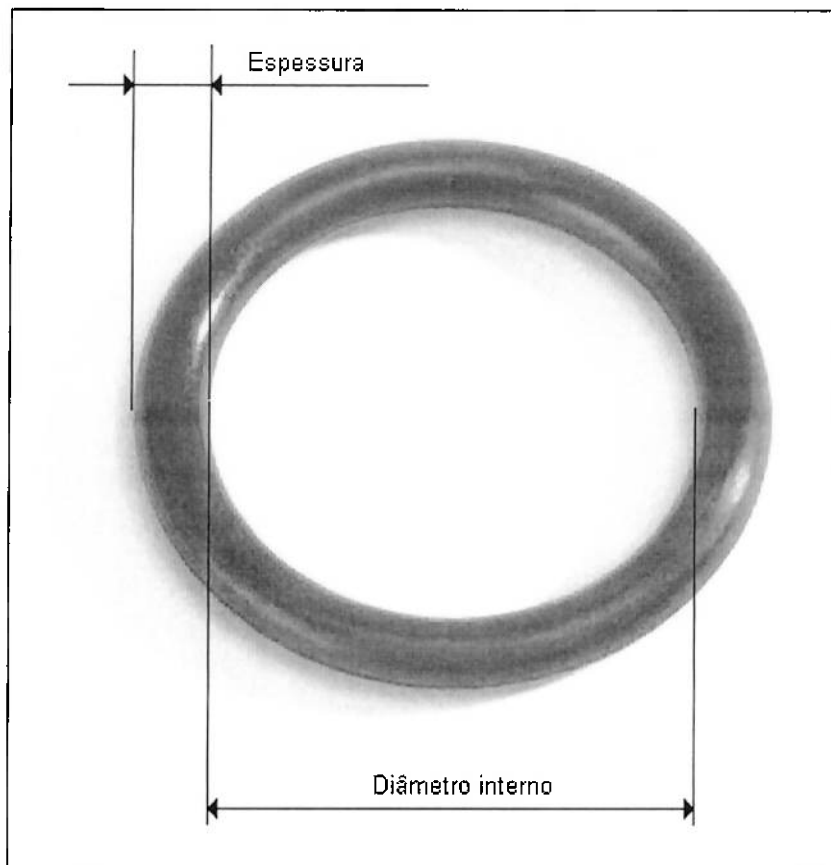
Exemplo de anel de vedção (*O-ring*)
